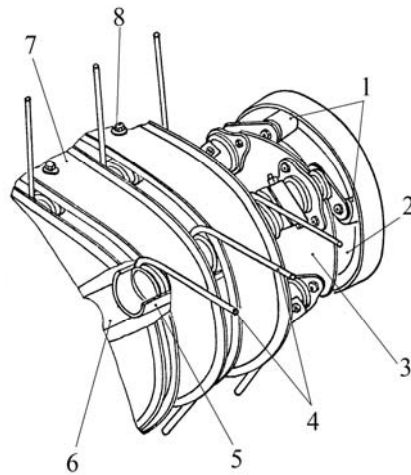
Барабан подбирающий подборщика: 1 – ролики; 2 – дорожка направляющая; 3 – диск; 4 – зубья пружинные; 5 – граблина; 6 – вал; 7 – скат; 8 – болт
